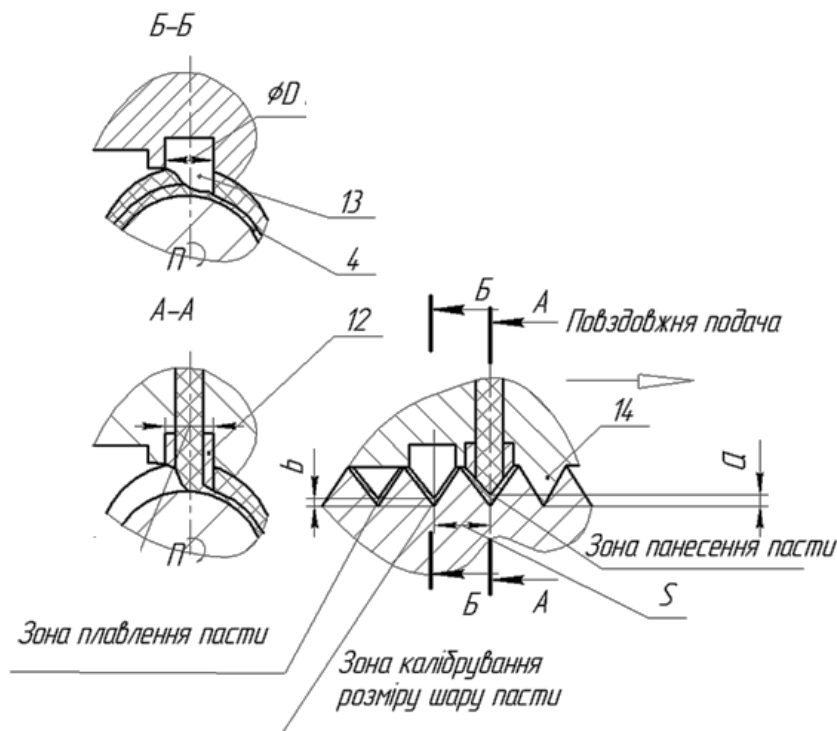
Схема нанесення на різьбову поверхню легкоплавкого сплаву: 12 – сопло; 13 – різьбовий елемент; 14 – копіювальний різьбовий елемент
